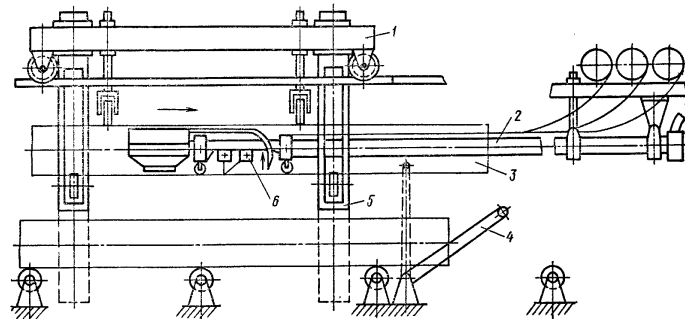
Схема стана для сварки внутренних швов труб:
